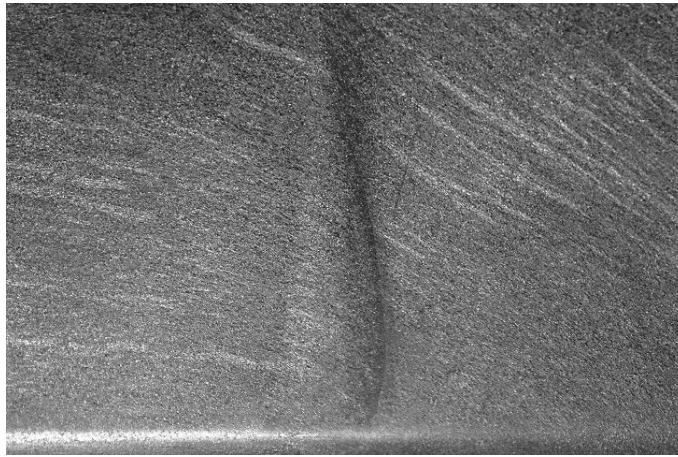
Aggrandissement au voisinage de la ligne de soudure
